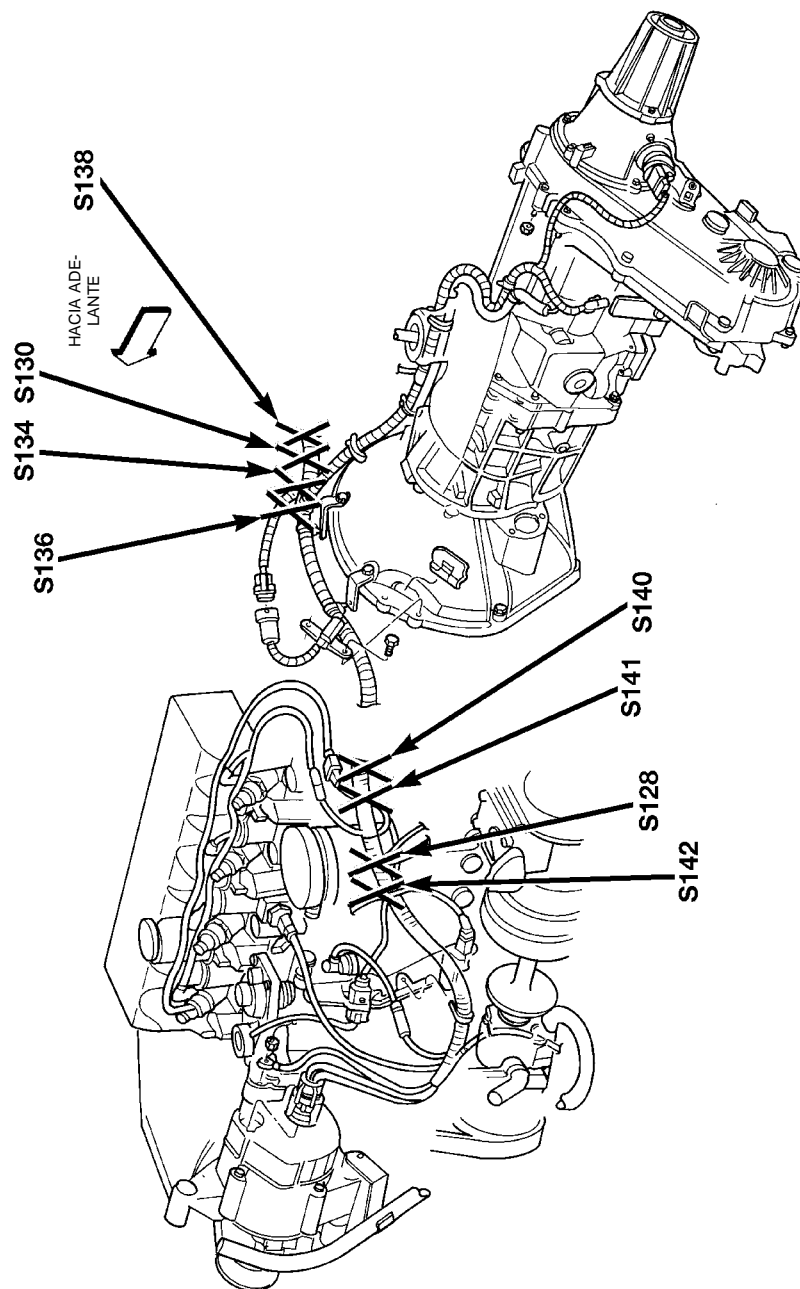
Empalmes del cableado del motor y la transmisión—Motor diesel
